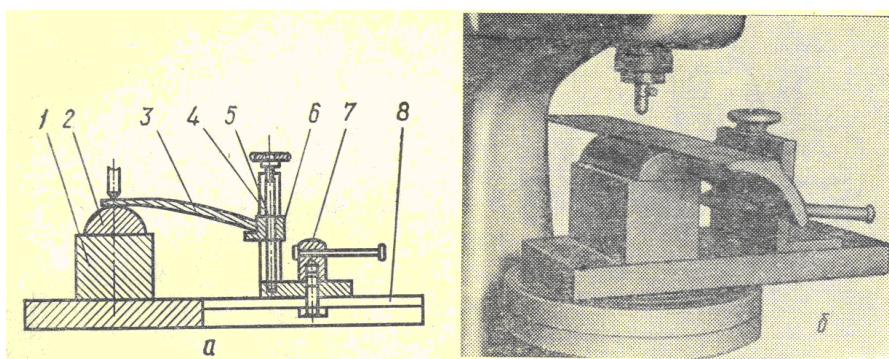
Приспособа для вимірювання деталей перемінного профілю: а – схема приспособи; б – розположення приспособи на твердомірі Роквела: столик-підставка (1); опорний столик (2); леміш (3); кронштейн (4); гвінт (5); упор (6); кронштейн (7); основа (8).
